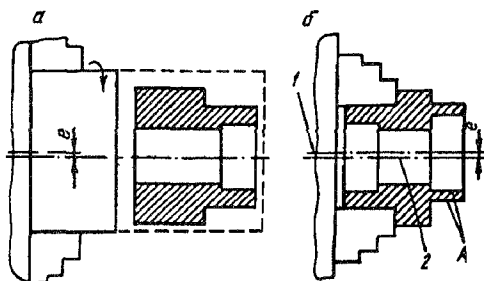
Схемы передачи смещения e установочно-зажимных элементов приспособления обработанной детали
